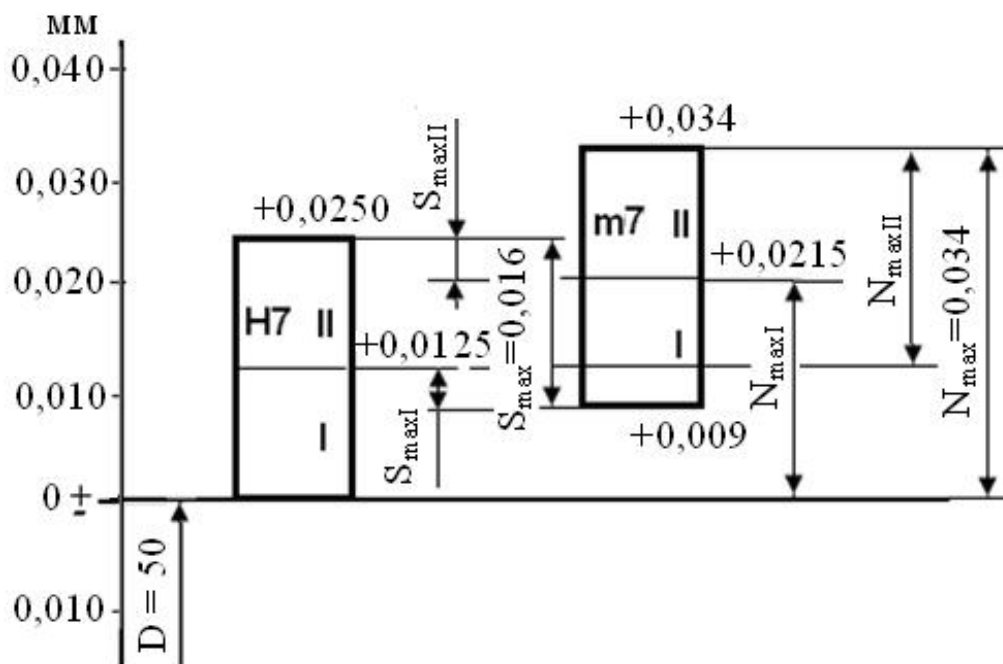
Схема полів допусків з'єднання  $\varnothing 50H7/m7$
